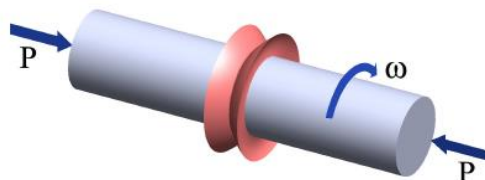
Procédé de soudage par friction rotative [14].
